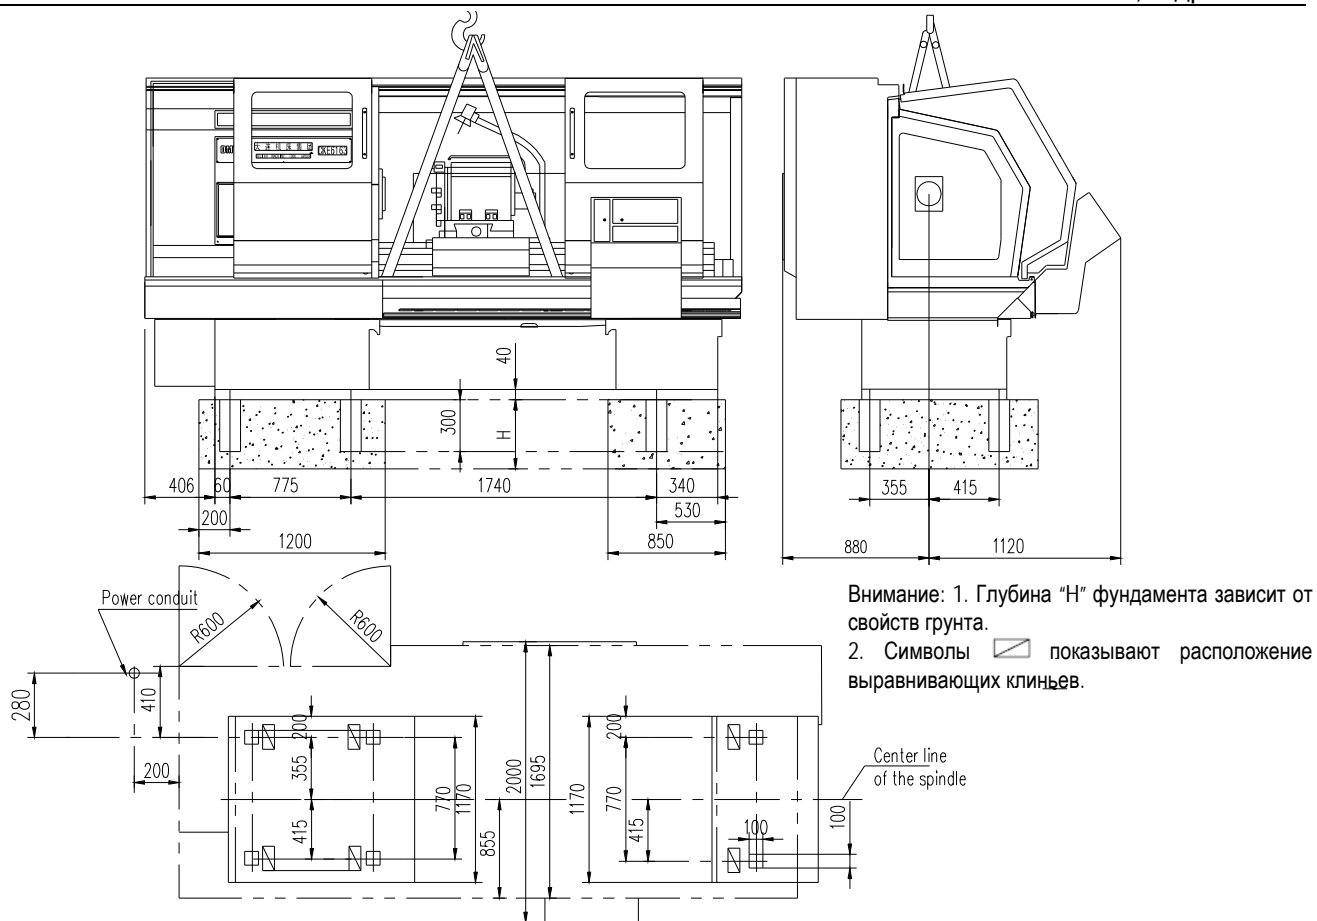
(стр. 1) Транспортировка и установка (для 1000)
